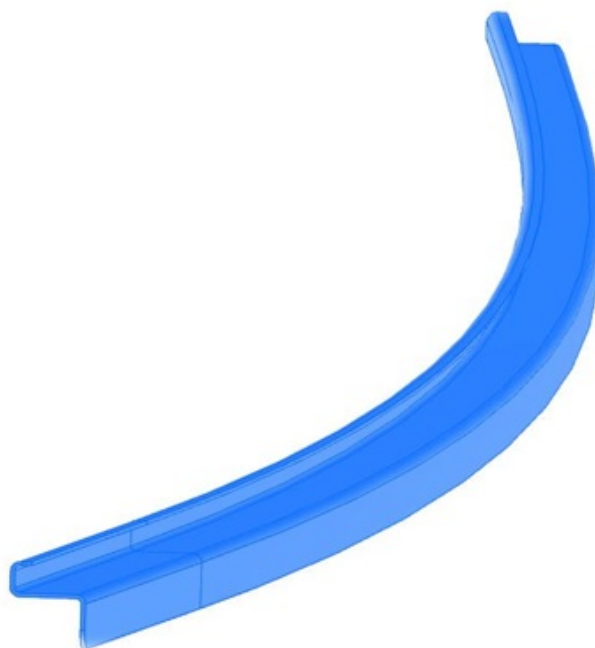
Заготовка стрингера из Z-образного гнутого профиля панели фюзеляжа самолета с переменными радиусами кривизны.
